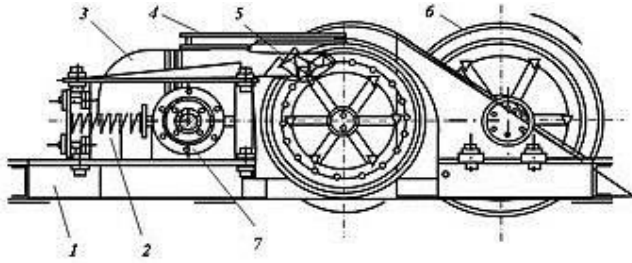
Двовалкова зубчаста дробарка типу ДДЗ
